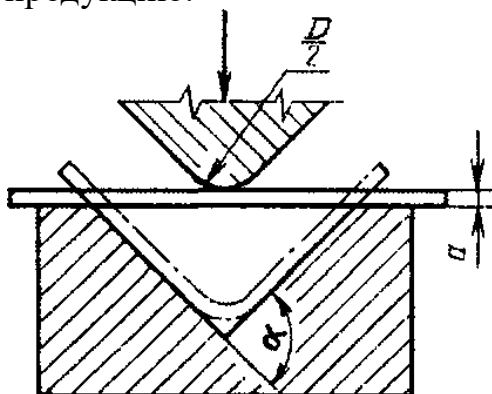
Схема приспособления (матрица с V-образным углублением и оправкой) для испытания на изгиб
